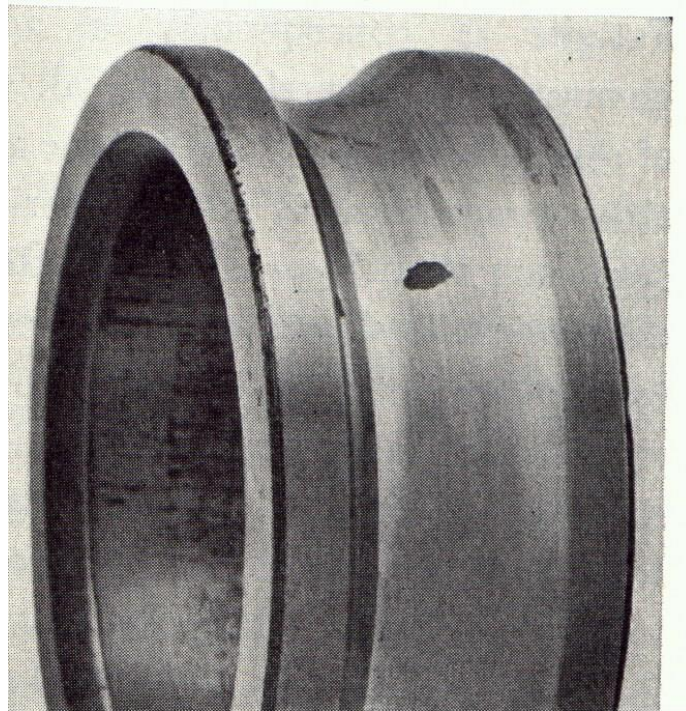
exfoliación por fatiga en la zona de rodadura de un aro interno de un rodamiento de bolas [2].
